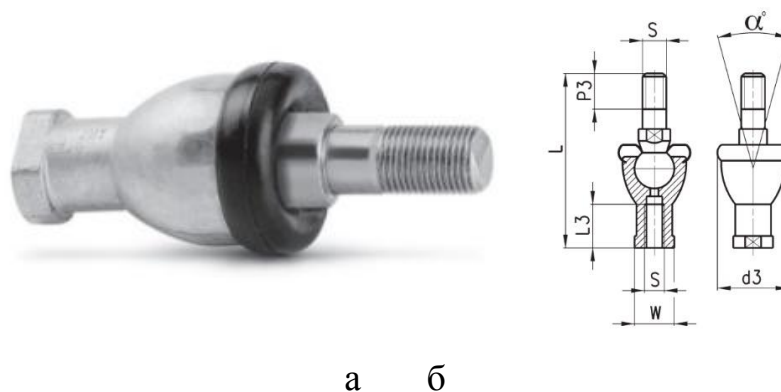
Кульовий шарнір пневмоциліндра серії 40 DIN/ISO 6431 а – загальний вигляд шарніра, б - схематичне креслення шарніра
